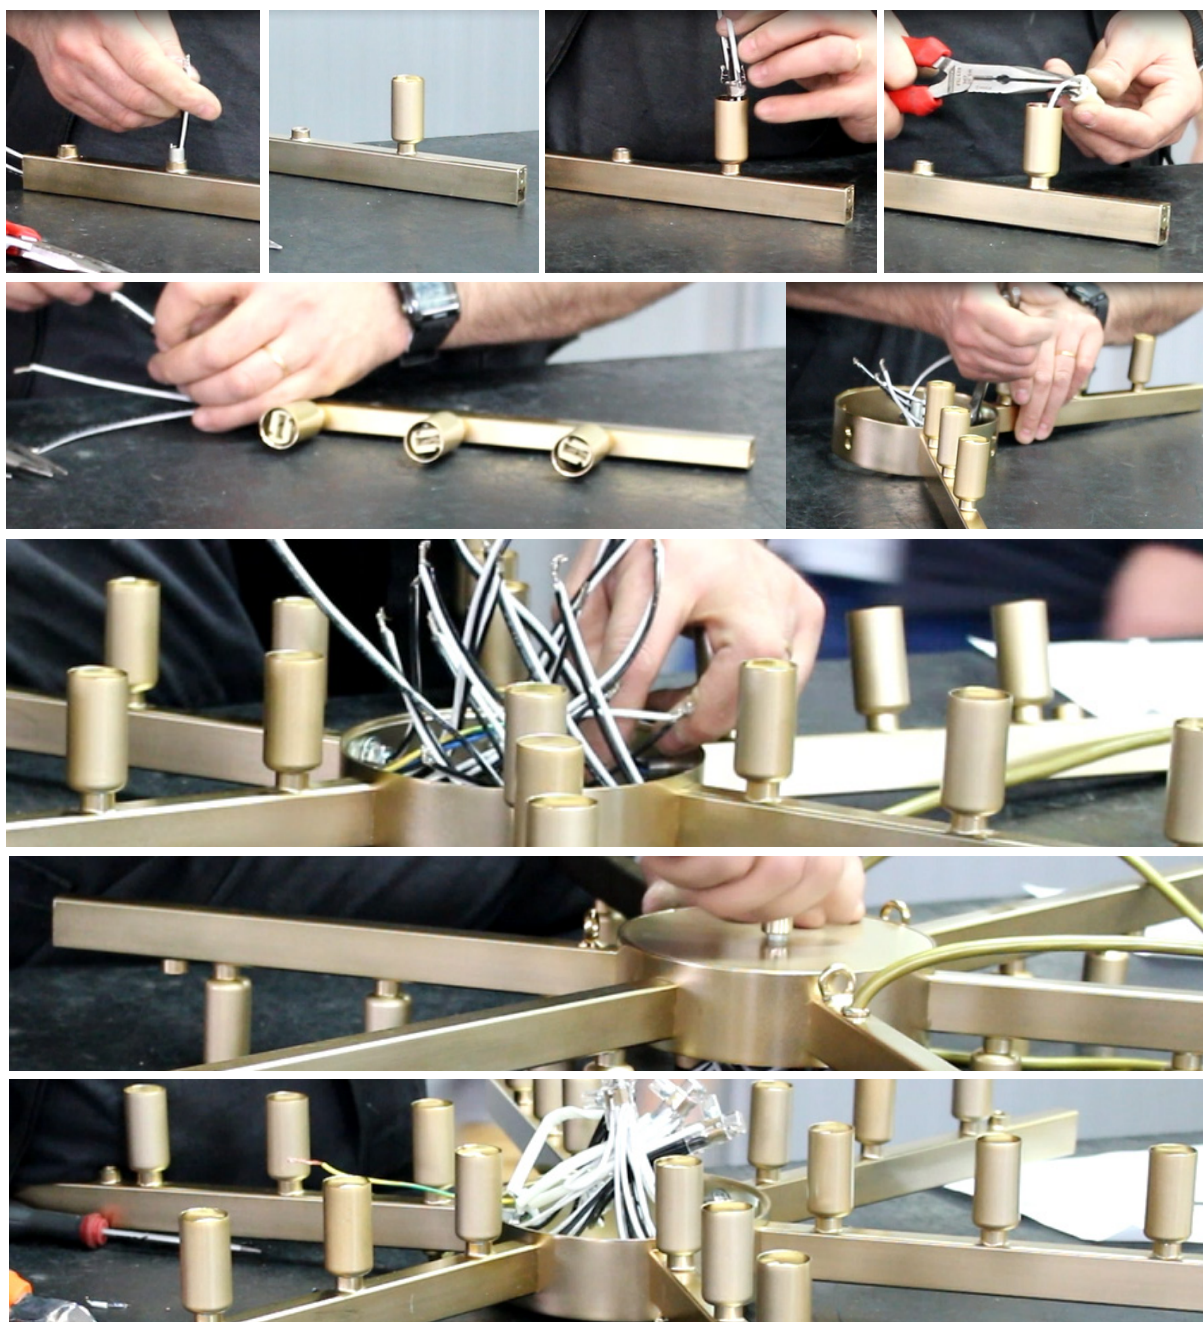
Conjunto de imagens do processo de montagem dos componentes do produto 2.
